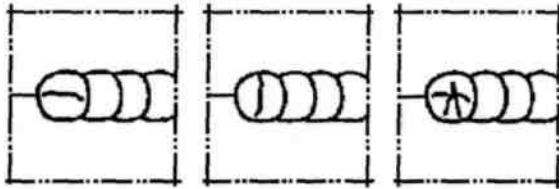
13. Кратерные трещины сварного соединения
